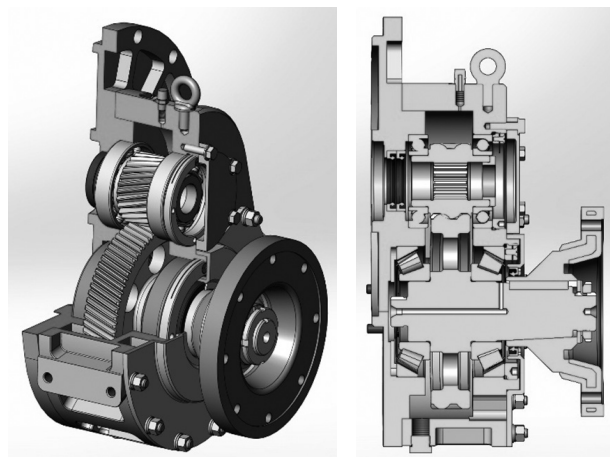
Внешний вид (а) и разрез (б) редуктора ВСП-1/1
